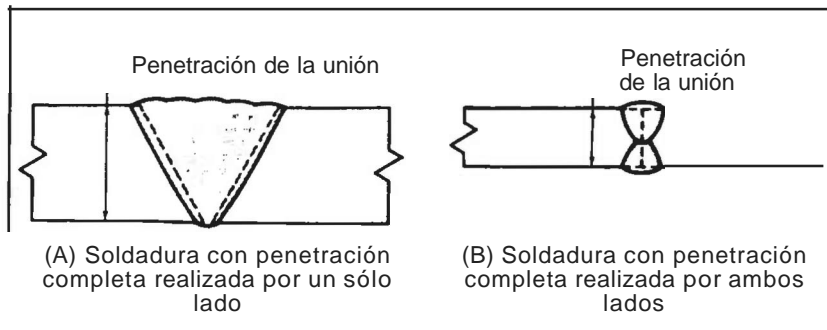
SOLDADURAS CON PENETRACIÓN COMPLETA
